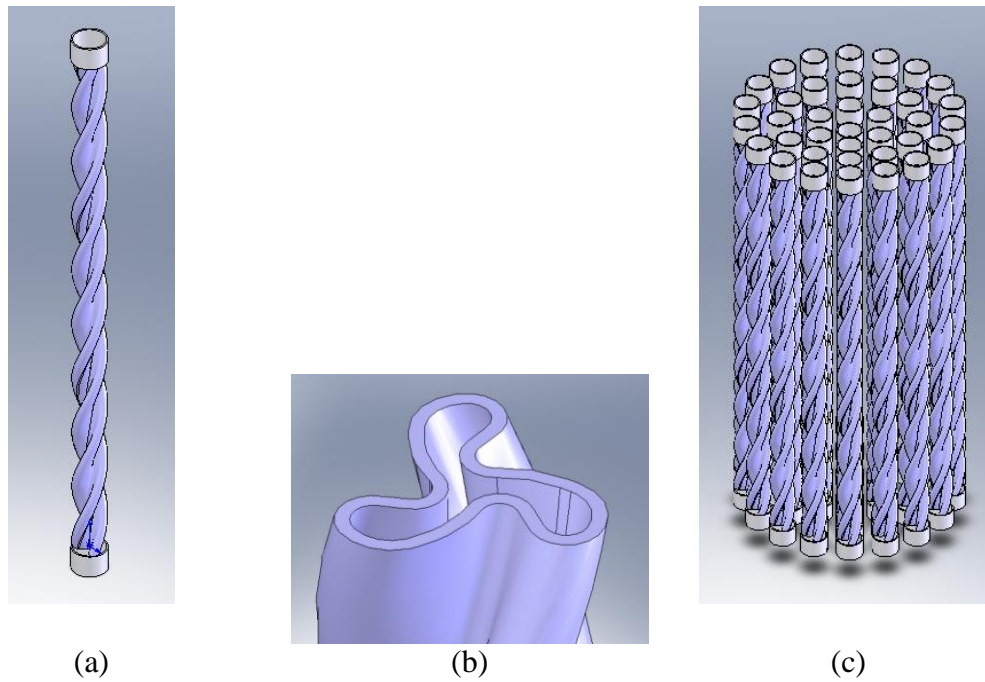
10– Immagini del fascio tubiero (a) tubo intero, (b) tubo in sezione e (c) disposizione tubi nel fascio tubiero
